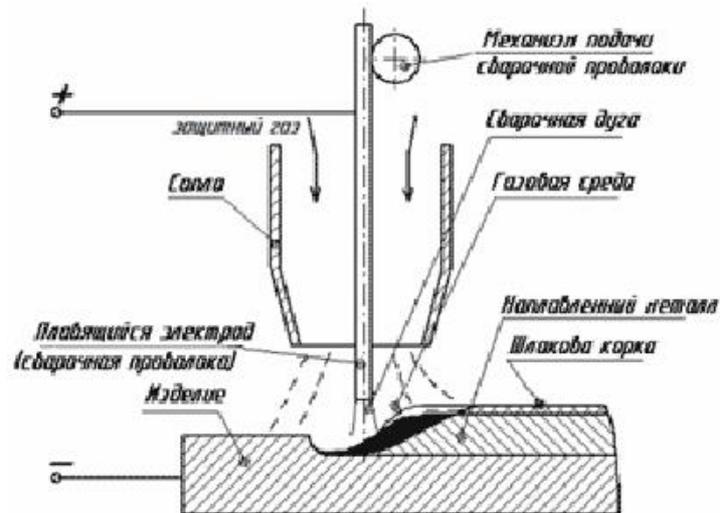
Схема сварки в защитных газах
